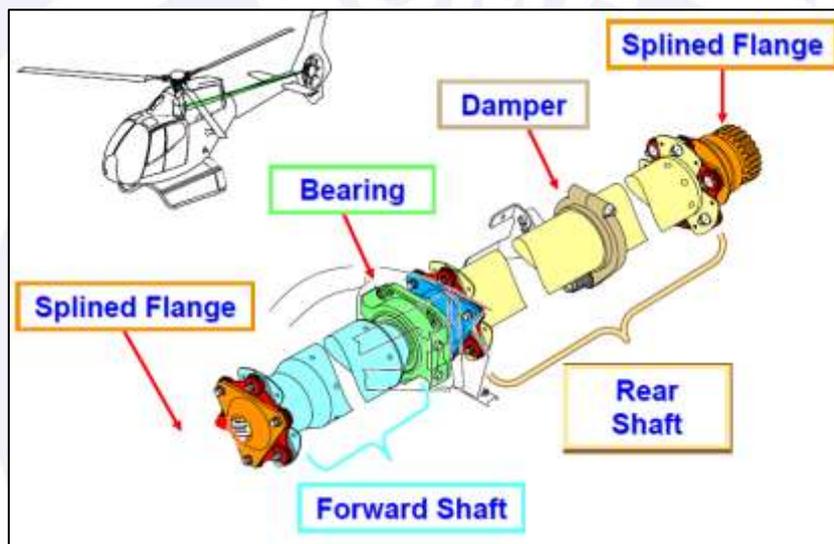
Ilustração do Eixo de Transmissão do Rotor de Cauda.
